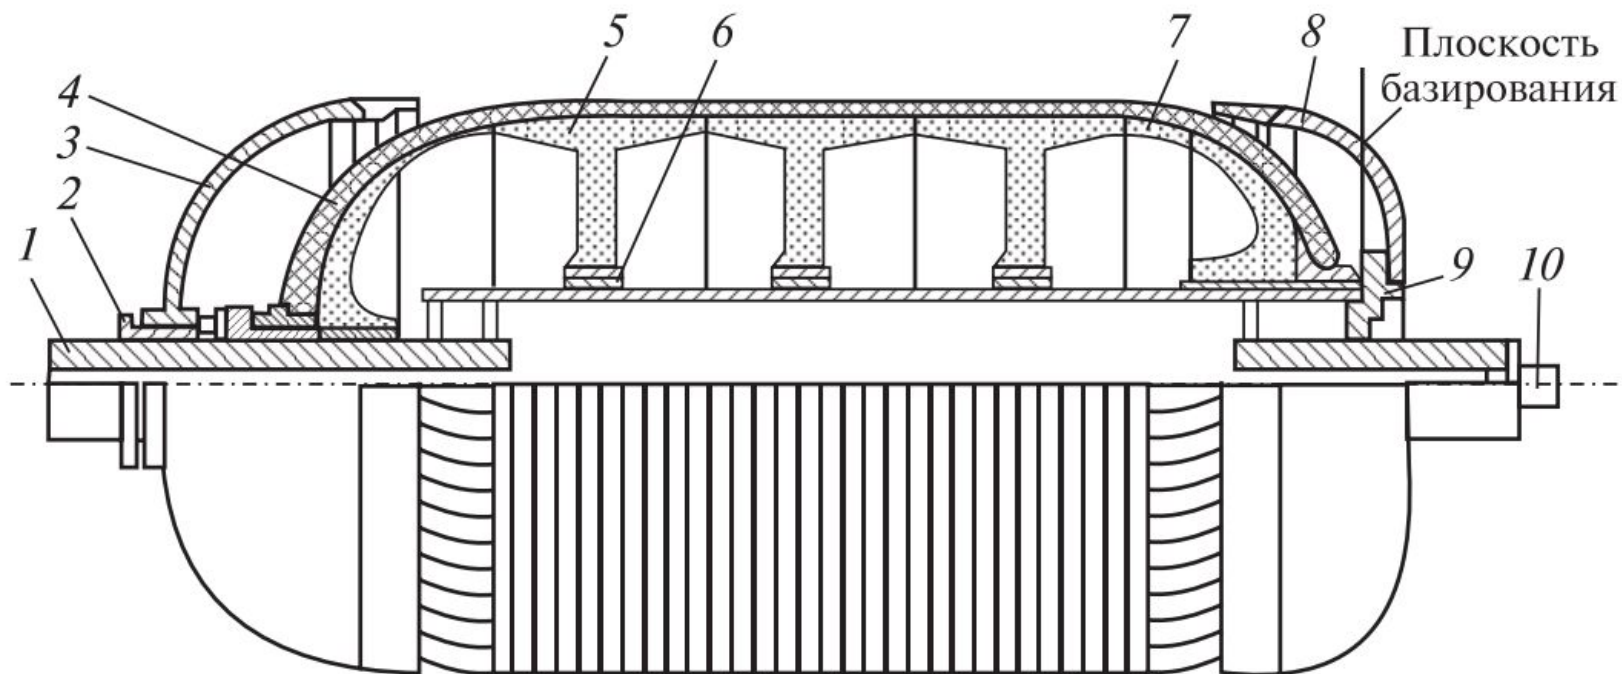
Конструкция оправки для намотки силовой оболочки корпуса РДТТ “юбками”.
